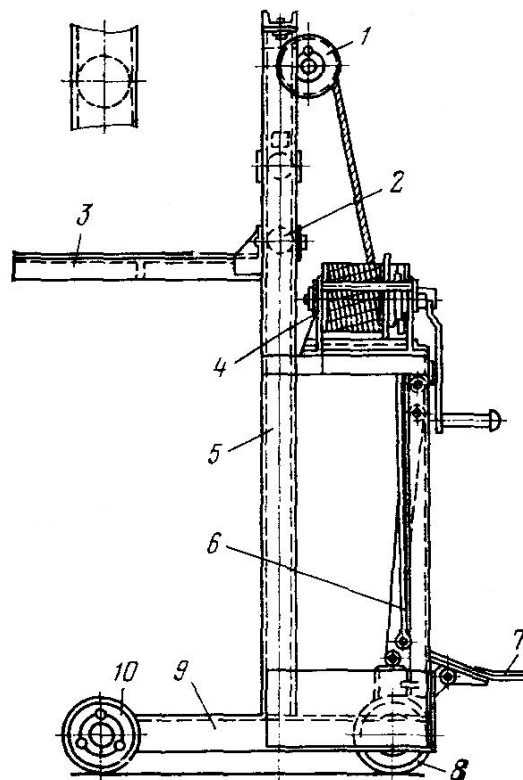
Рухомий підйомник з ручним приводом: 1-поліспаст; 2-ролики напрямні; 3-стіл підйомний; 4-лебідка ручна; 5-напрявні; 6-дишло; 7-педаць; 8-колеса спарені передні; 9-рама; 10-колеса задні
